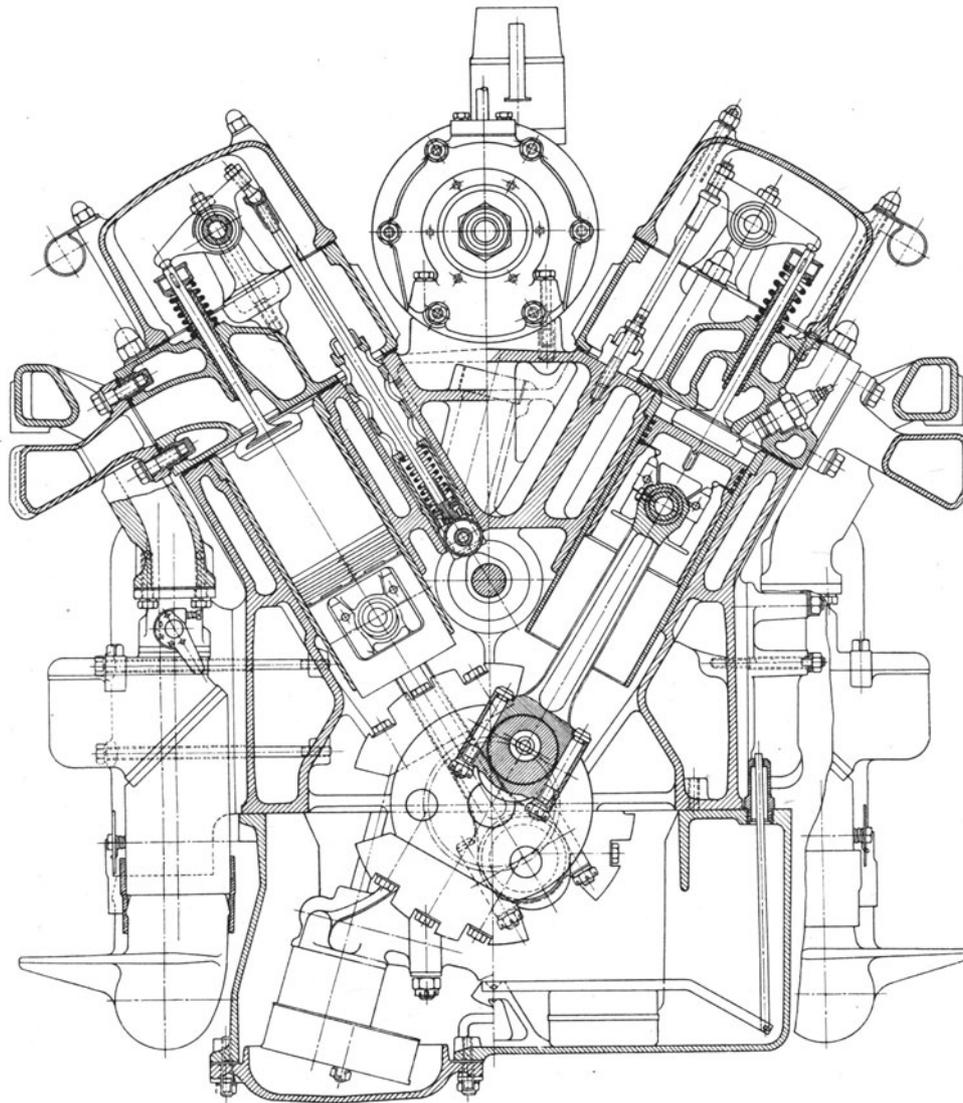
12-Zylindermotor DSO 8 der Maybach Motorenbau G. m. b. H.
